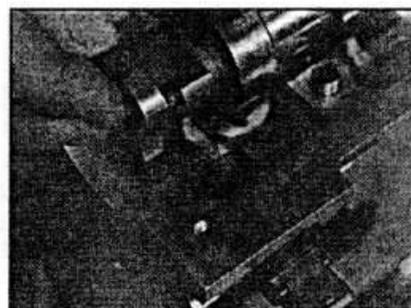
С.28. Распределительный вал, управляющий впускными клапанами имеет выступ для датчика положения вала.
